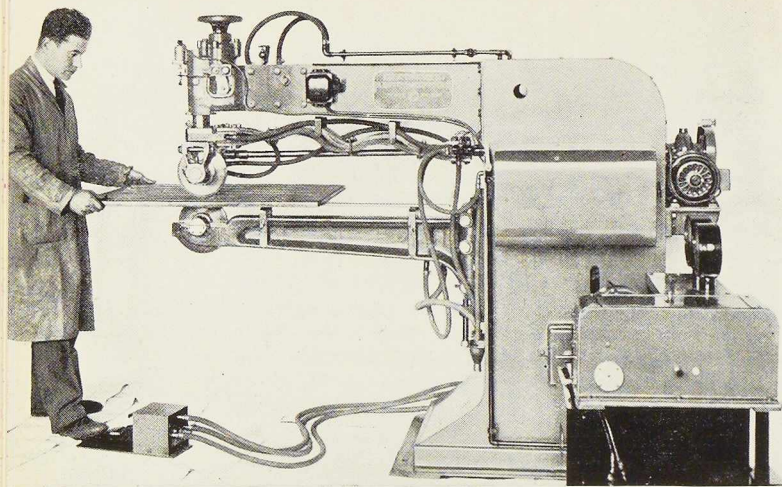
Machine pour souder au galet les radiateurs en tôle.
